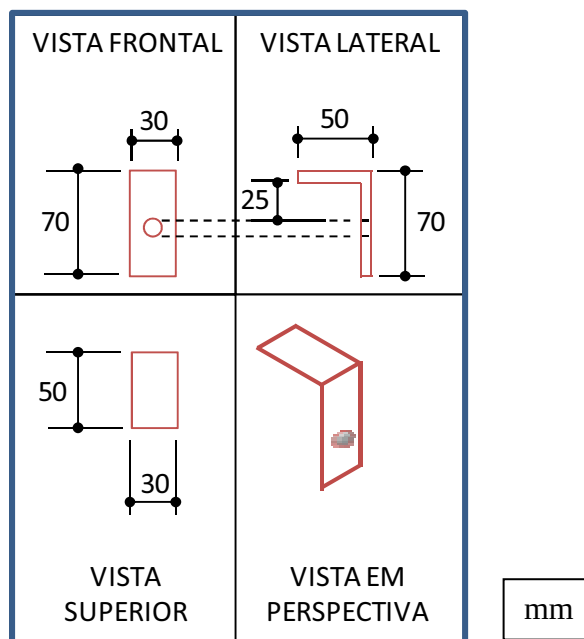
Desenho técnico da cantoneira de fixação da armadura.
